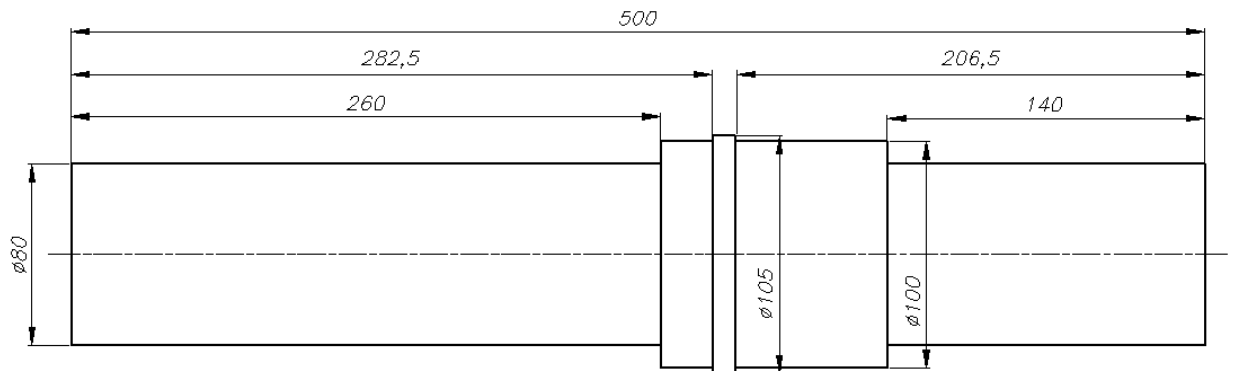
Dimensiones preliminares del árbol de transmisión
